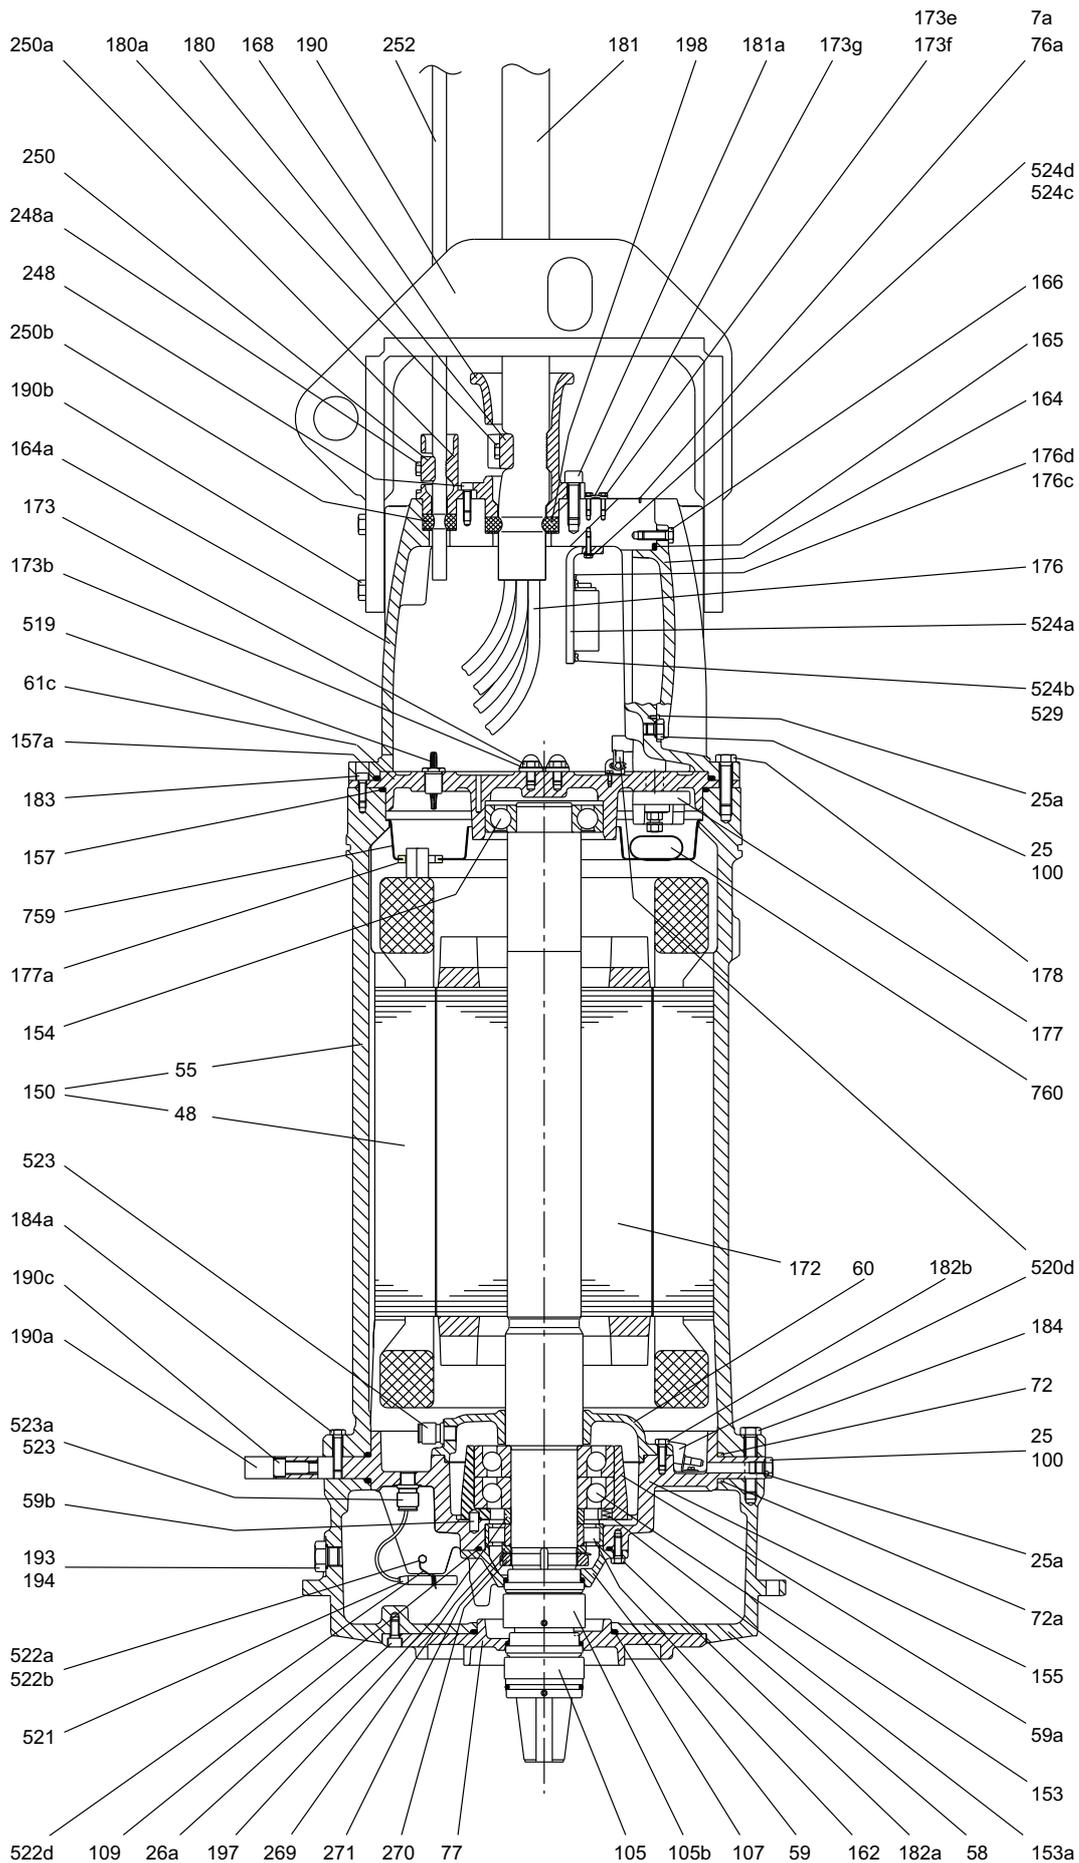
Взрывозащищённый электродвигатель без охлаждающего кожуха
